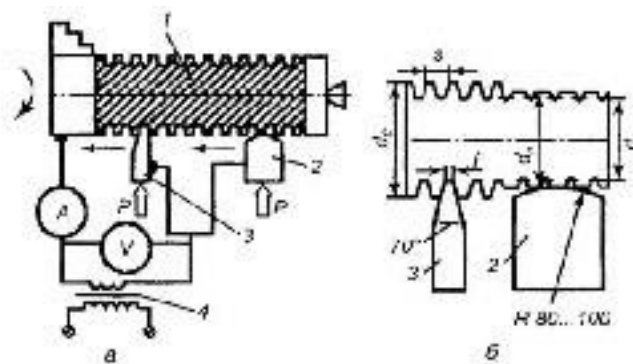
Пластическое деформирование электромеханической обработкой: а — схема обработки; б — схема высадки и сглаживания; 1 — деталь; 2 — сглаживающая пластина; 3 — вытесняющая пластина; 4 — понижающий трансформатор
